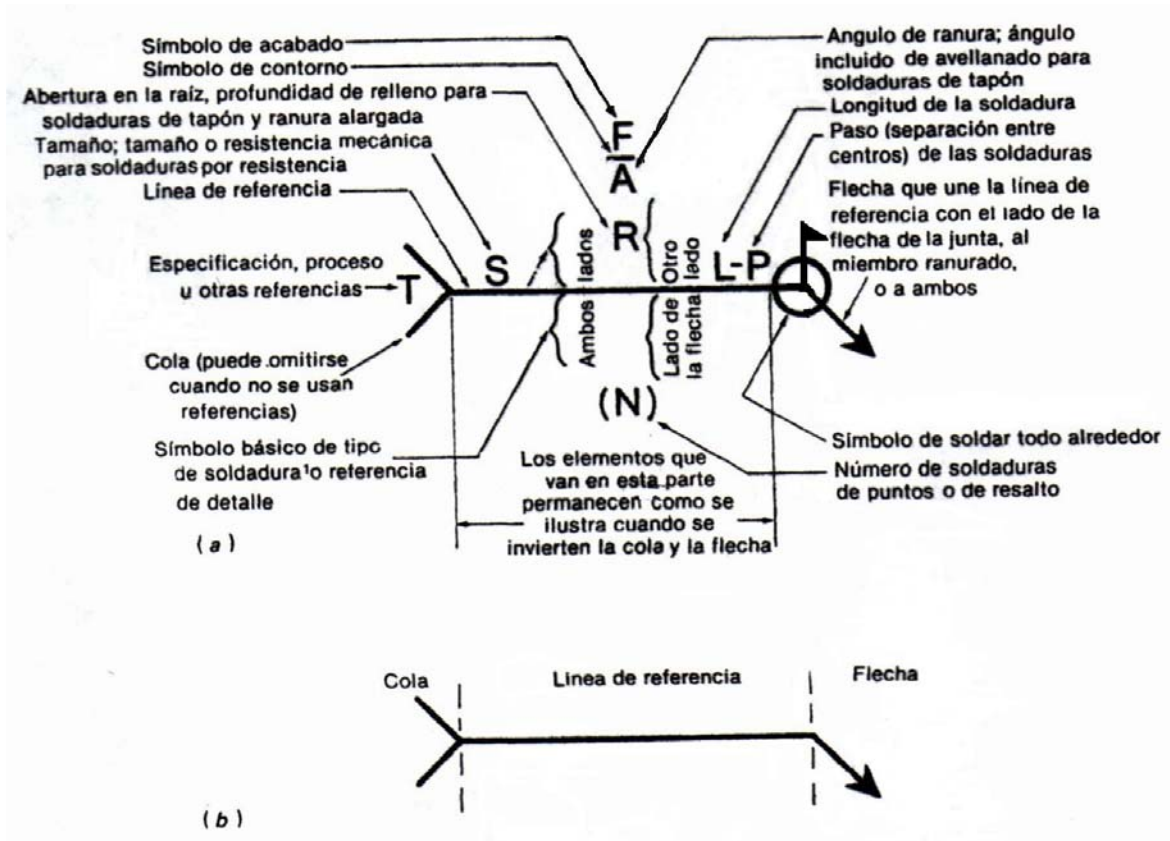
(a) Símbolo completo de la soldadura. (b) La cola, la línea de referencia y la flecha: el símbolo básico de la soldadura.
